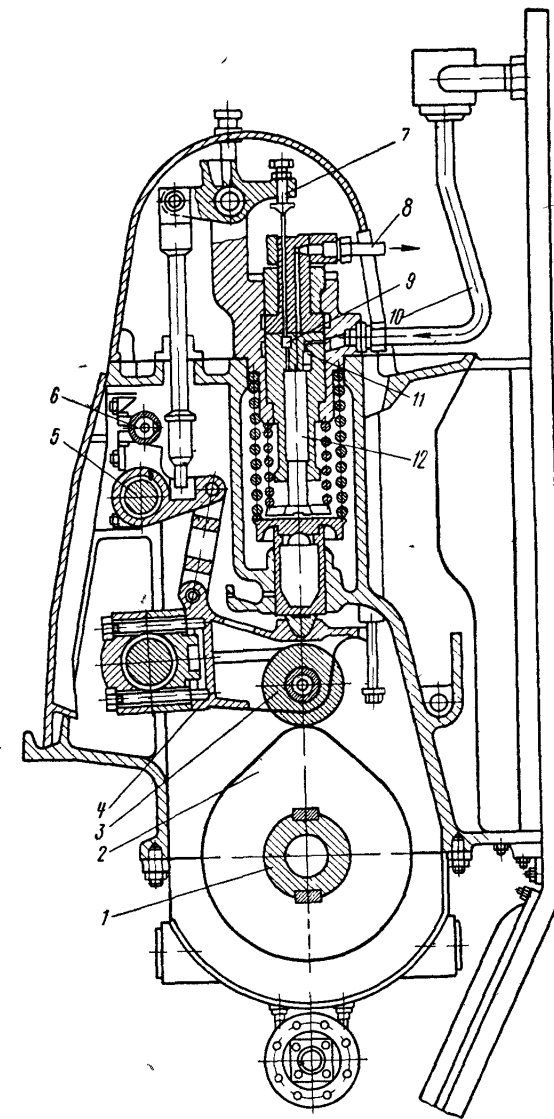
Топливный насос двигателя «Фиат» 750S. 1 — распределительный вал, 2 — кулачковая шайба, 3 — рычажный толкатель, 4 — прокладка регулировочная, 5 — эксцентриковый вал, 6 — валок для выключочной, 7 — регулировочный болт; 8 — трубопровод насоса, 9 — регулировочный клапан; 10 — трубопровод нагнетательный, 11 — всасывающий клапан, 12 — плунжер
